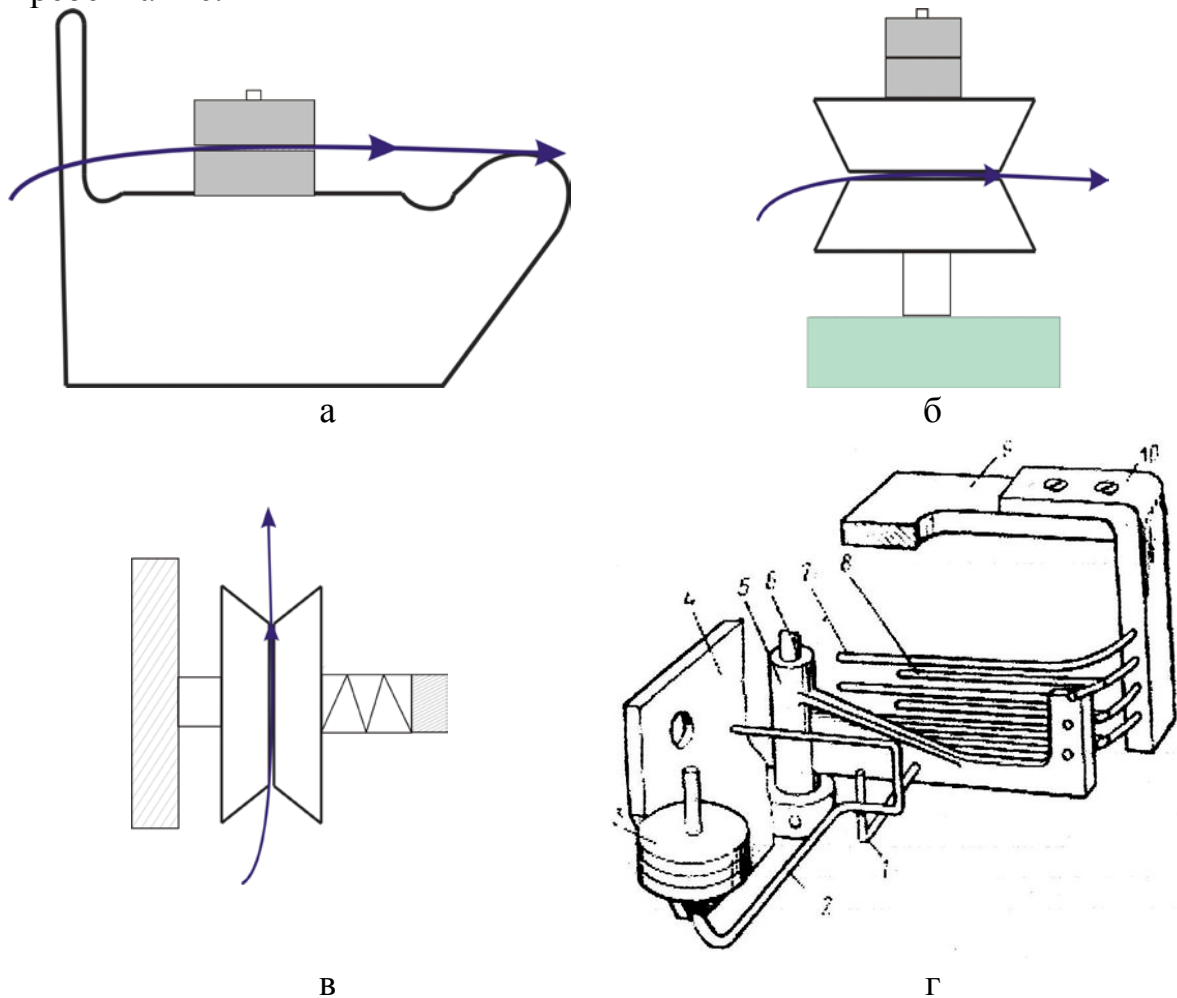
Натяжные приборы: а) шайбовый; б), в), дисковый; г) гребенчатый
